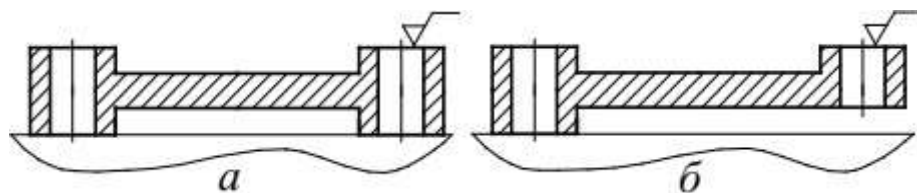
Конструкція деталей з опорними поверхнями:
